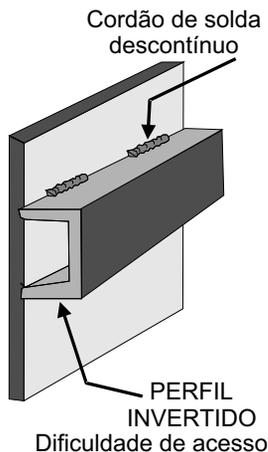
Cordões de solda descontínuo favorecem a corrosão em frestas
